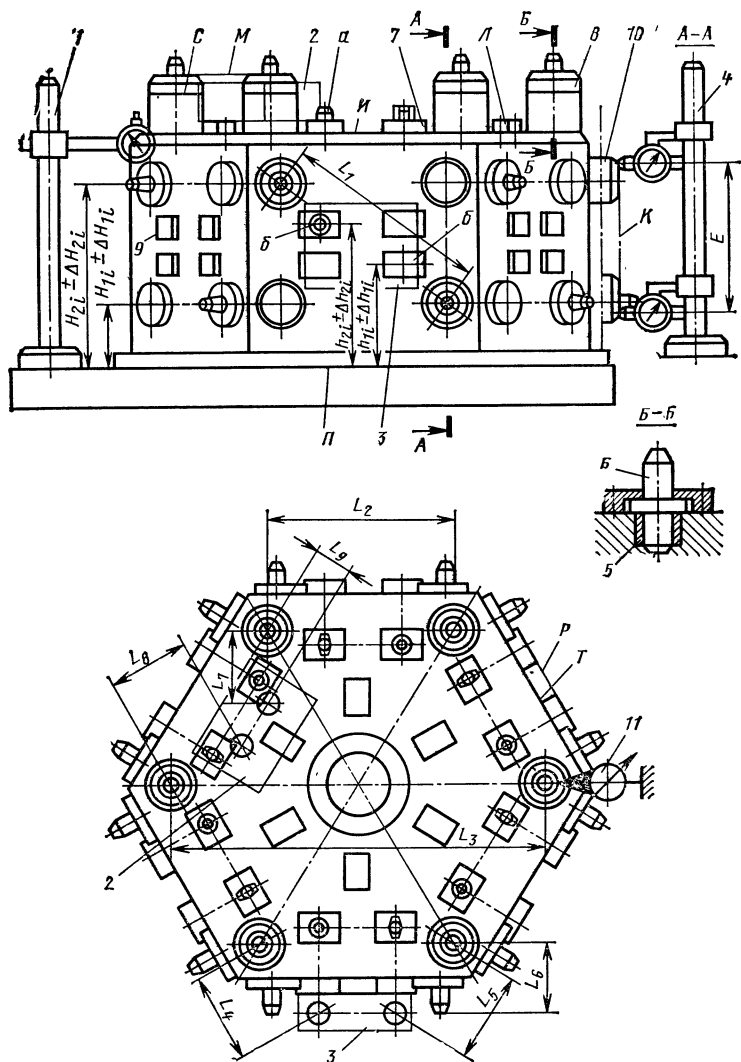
Контролируемые параметры геометрической точности многопозиционных многоместных приспособлений АС (а и б — пальцы базирования обрабатываемой детали на верхней или боковой поверхности приспособления), позиции см. табл. 37
